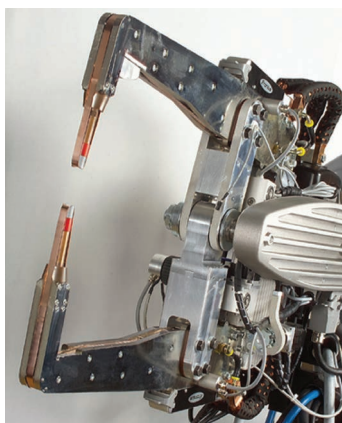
Сварочные клещи Delta Spot — Fronius
